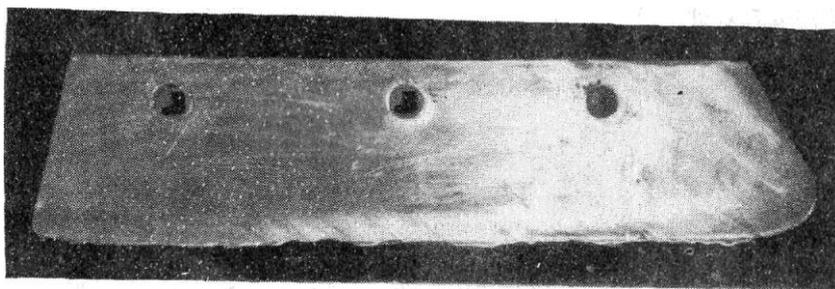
Выбракованный самозатачивающийся лемех
